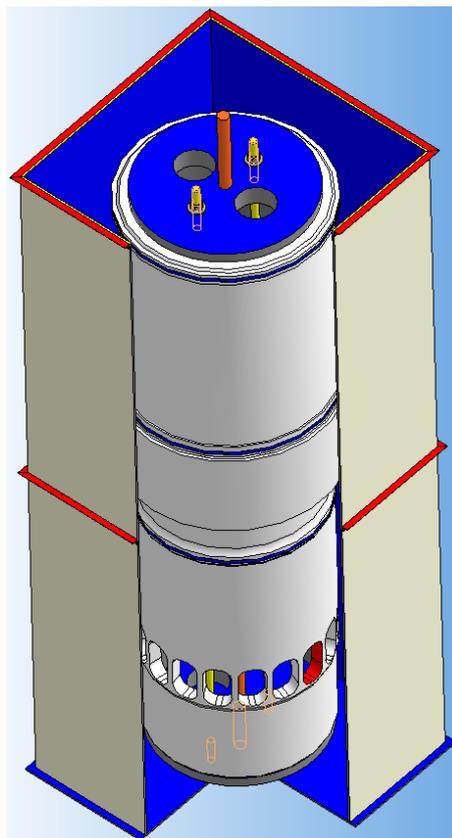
Пример установки втулки цилиндра двухтактного двигателя в моечную ванну с ультразвуковым генератором
